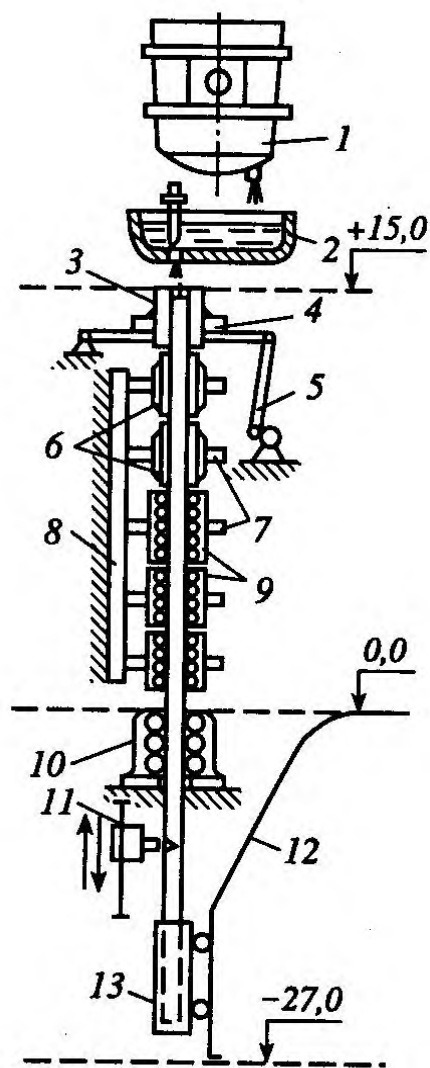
Схема вертикальной машины непрерывного литья заготовок:
